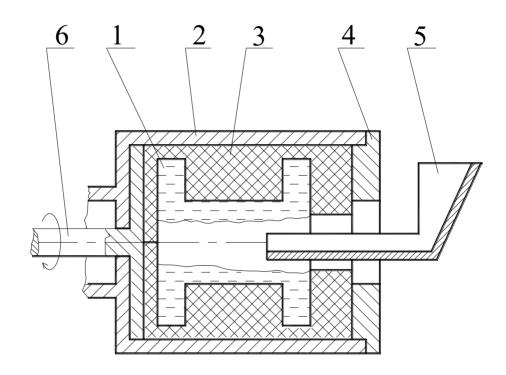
Форма металлическая для центробежного литья с горизонтальной осью вращения: 1 – отливка, 2 – форма металлическая, 3 – стержень песчаный разъемный, 4 – крышка торцевая, 5 – желоб для заливки, 6 – шток выталкивателя
